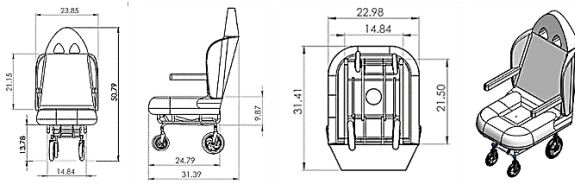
4d. Dimensiones de la silla de ruedas.
